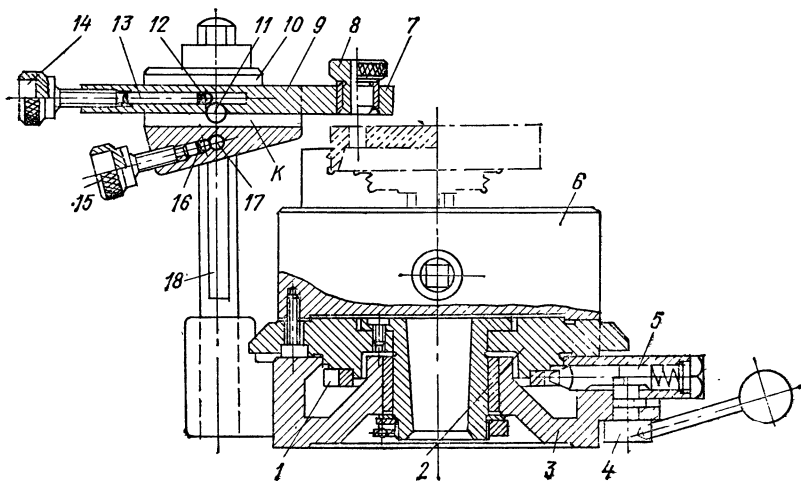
Переналаживаемый кондуктор с делительным устройством для обработки отверстий на торцах фланцев
